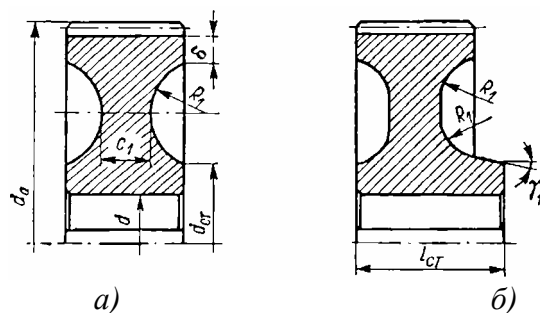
Конструкции штампованных цилиндрических зубчатых колес для редукторов
